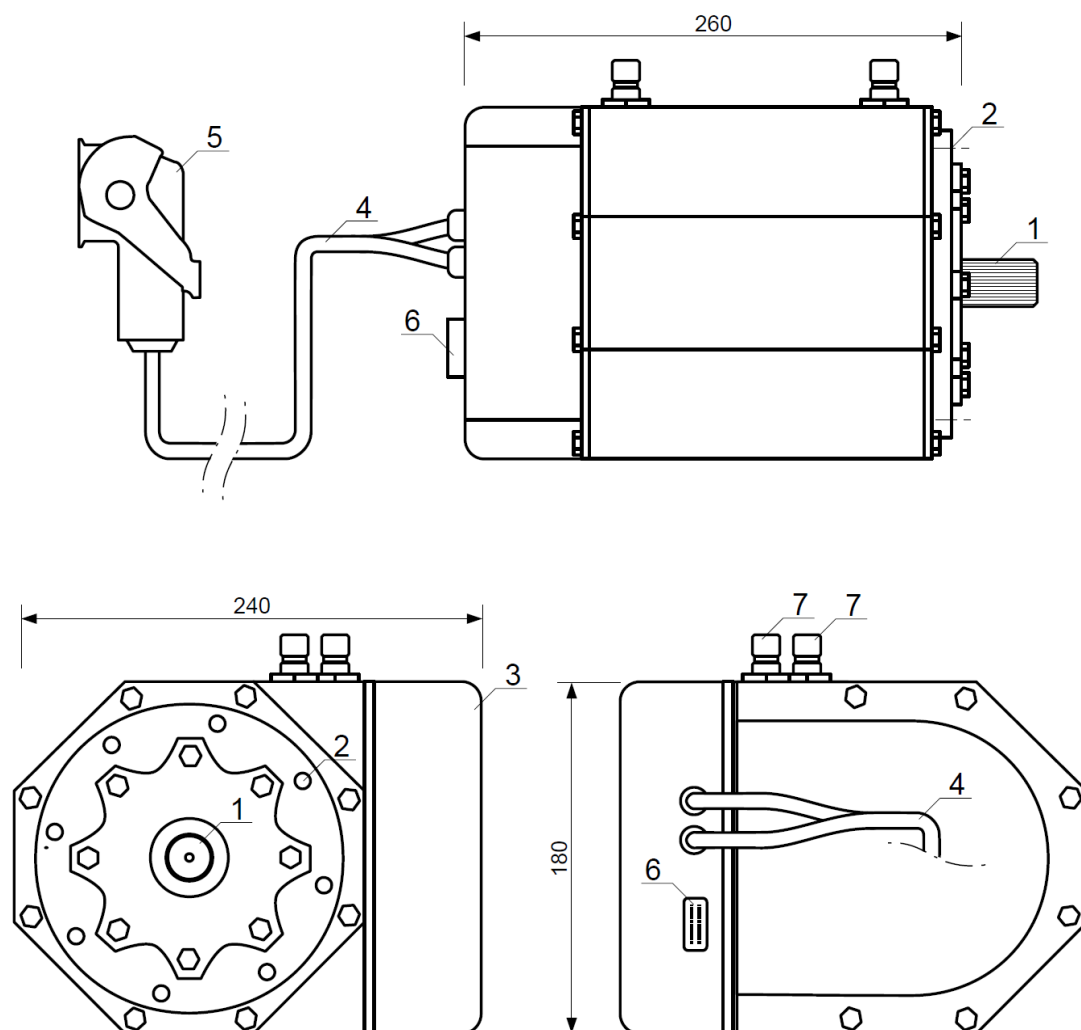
Внешний вид и размеры (mm) двигателей Capforce: 1 - вал; 2 - крепежные отверстия; 3 - DC-AC преобразователь; 4 - кабель питания; 5 - вилка для подключения питающего напряжения; 6 - разъем управления; 7 - патрубки для подвода охлаждающей жидкости.
